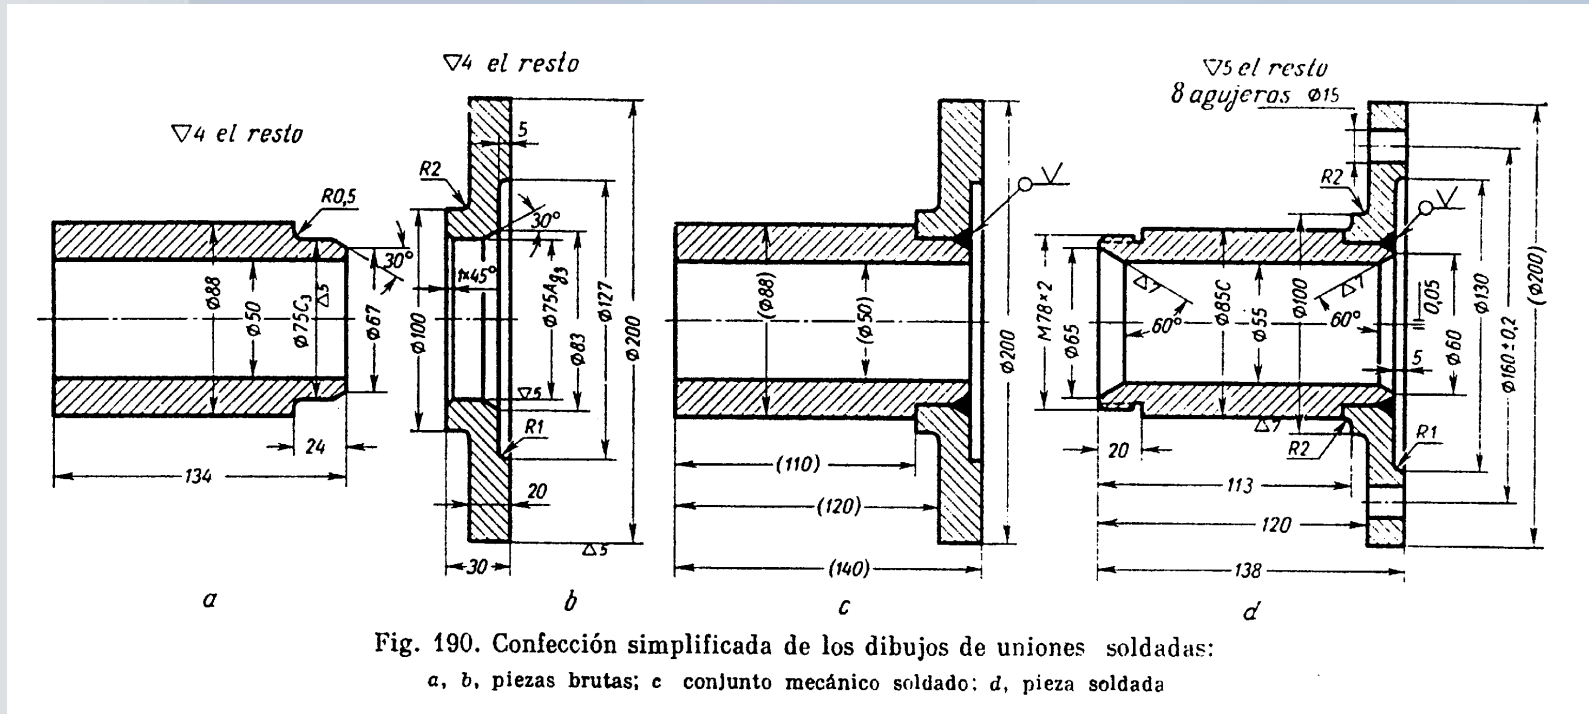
Confección simplificada de los dibujos de uniones soldadas:
